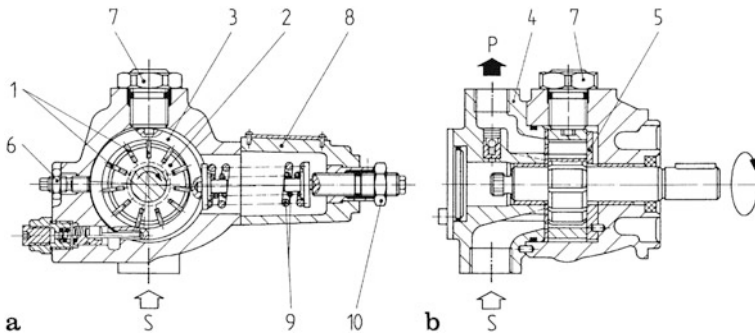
Flügelzellenpumpe mit Hubring, Einfachflügeln, direkt gesteuert über mechanischen Druckregler (Nullhubregler) (V 5, Bosch Rexroth). P Druckseite, S Saugseite, 1 Verdrängerflügel (Einfachflügel), 2 Rotor, 3 Hubring, 4 Deckel mit Steuerscheibe, 5 Axialscheibe, 6 Fördervolumeneinstellschraube, 7 Höheneinstellschraube, 8 Federgehäuse, 9 Stellfeder, 10 Druckeinstellschraube
